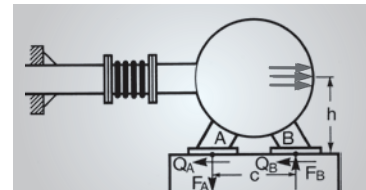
Axialkraft an einem Aggregat mit Axial-Kompensator
